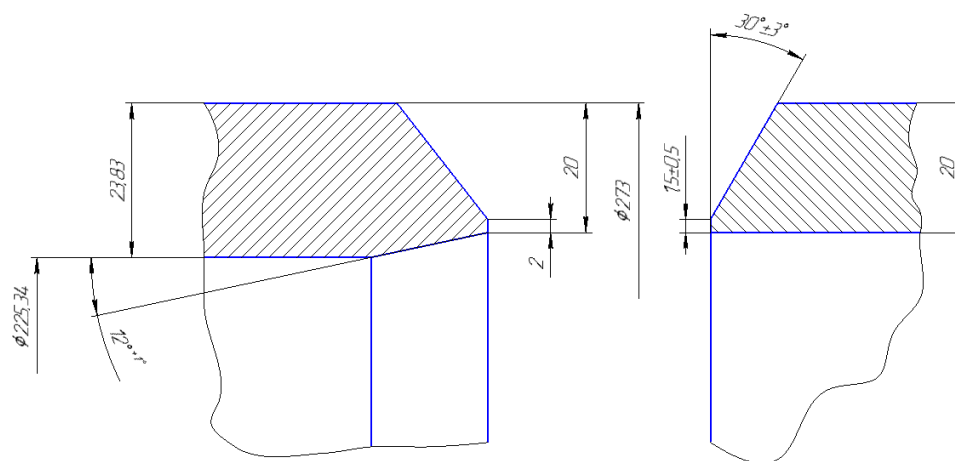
Подготовка поверхности труб перед выполнение сварки согласно размерам соединения С17 по ГОСТ 16037 (б) и заводского торца тройника (а)
